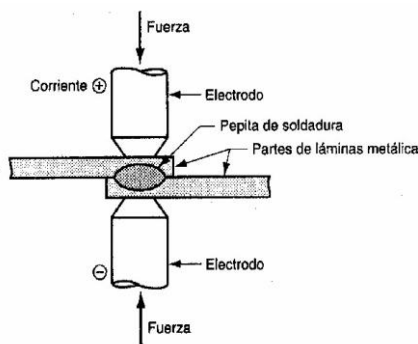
Esquema de Funcionamiento de una Soldadura RW
